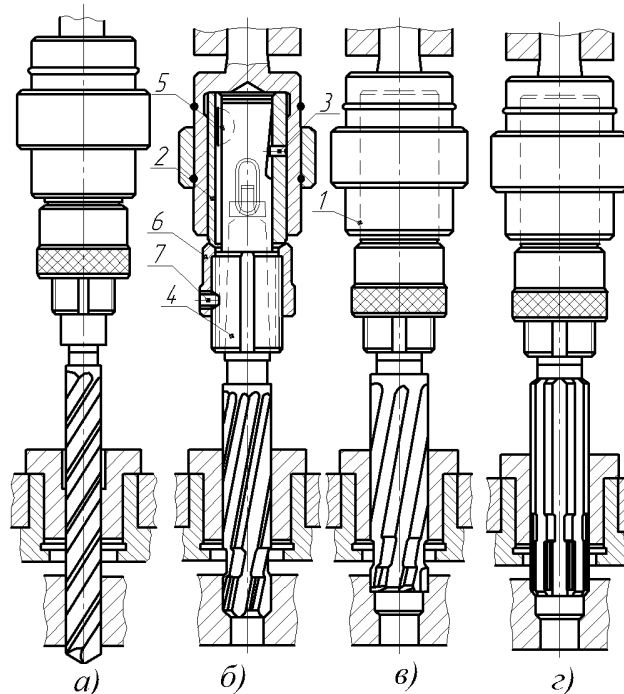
Схема послідовного оброблення отворів (свердління, зенкування чорнове, чистове і розвертування) на вертикальному одношпindelному свердильному верстаті з використанням швидкозмінного патрона:
